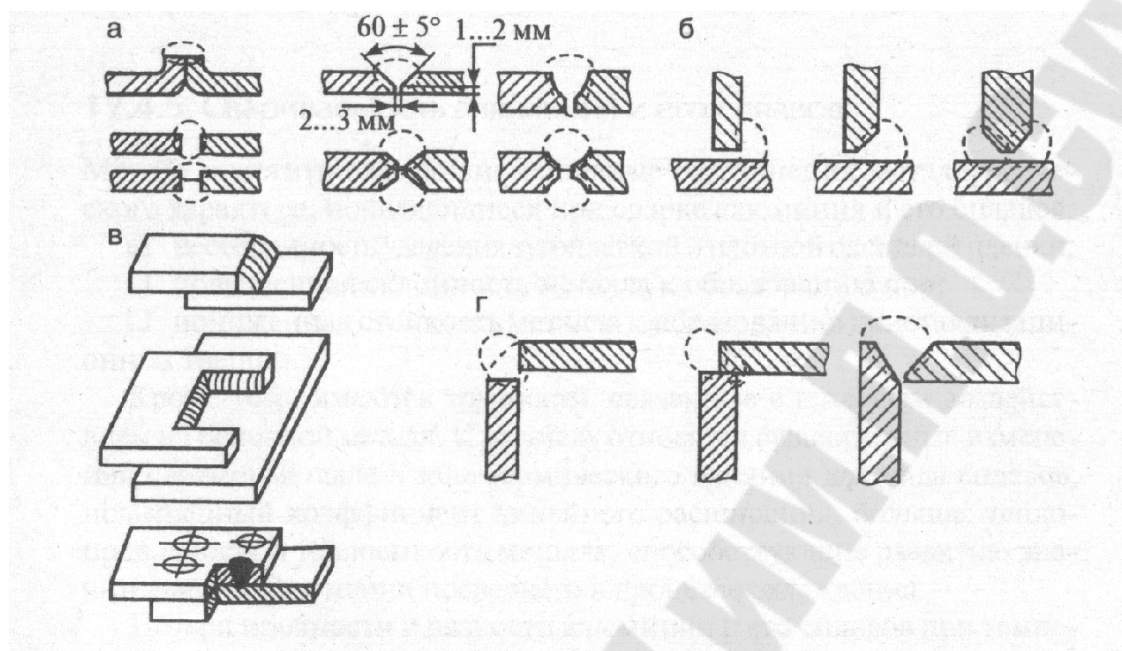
Типы сварных соединений: а – стыковое; б – тавровое; в – нахлесточное; г – угловое
